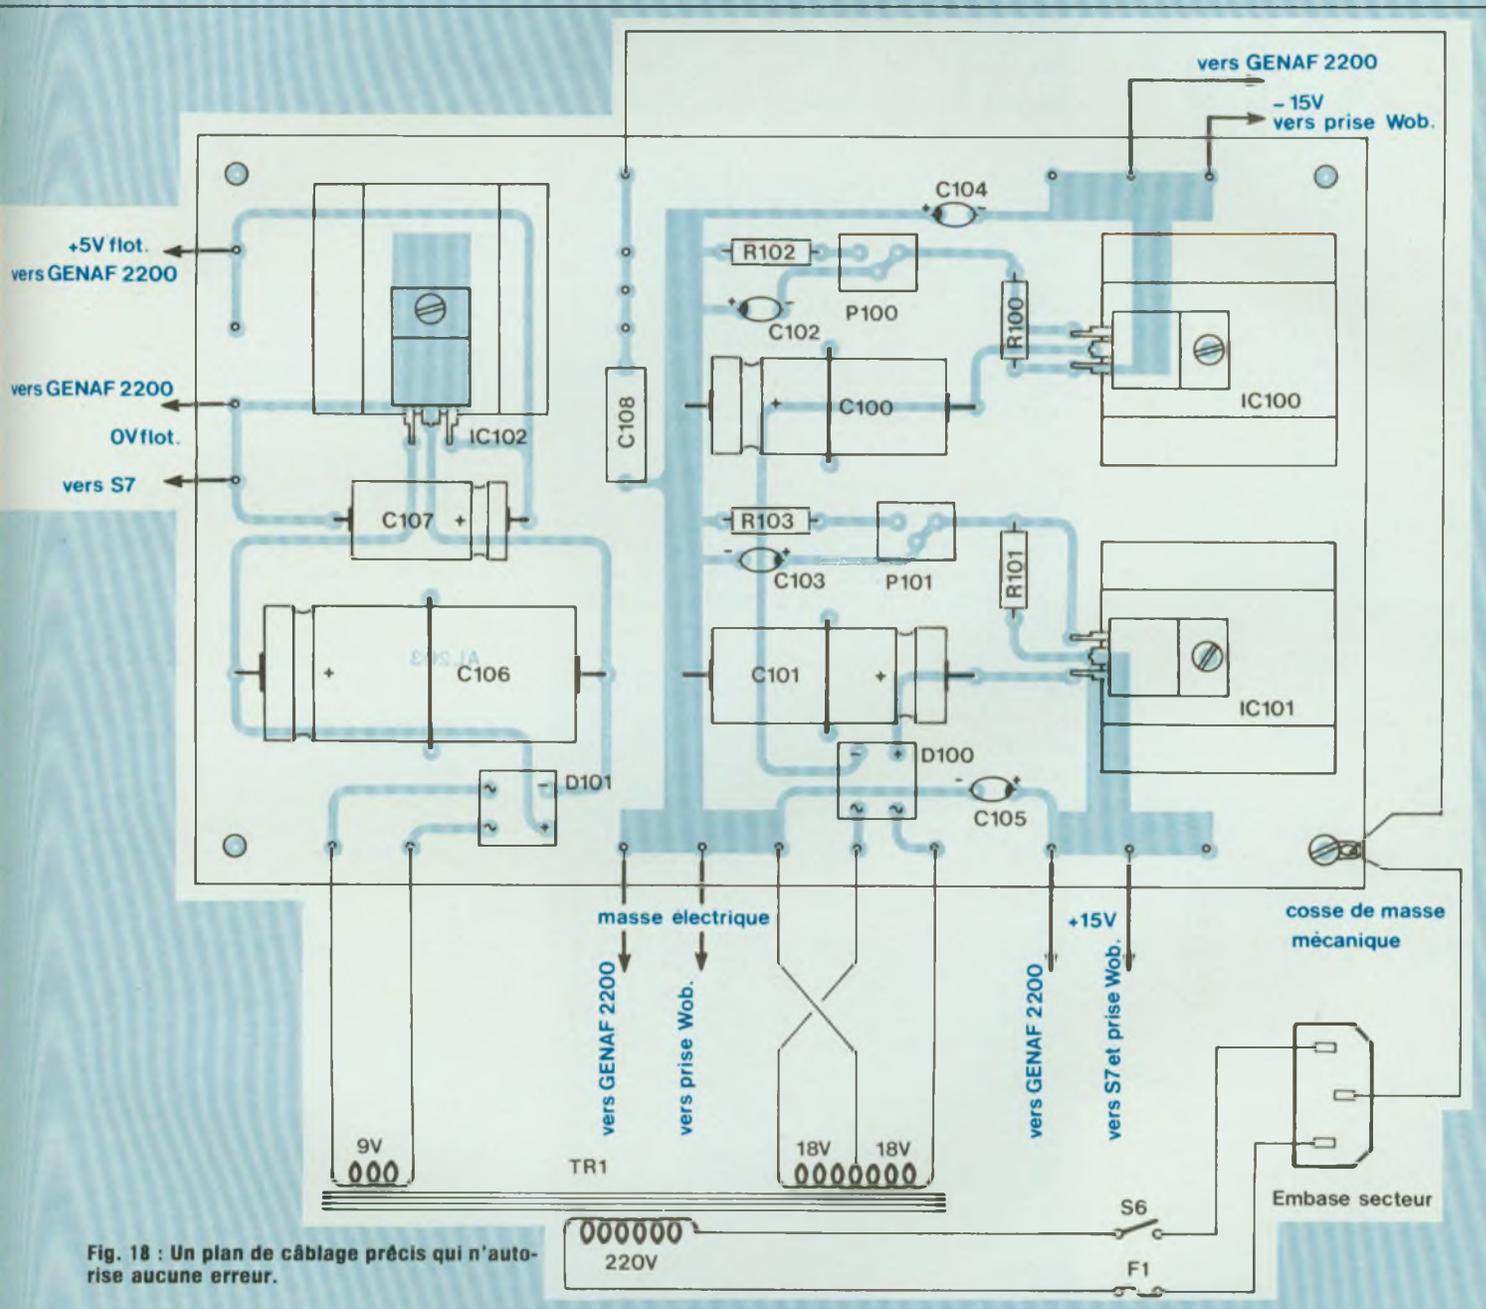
Un plan de câblage précis qui n'autorise aucune erreur.
